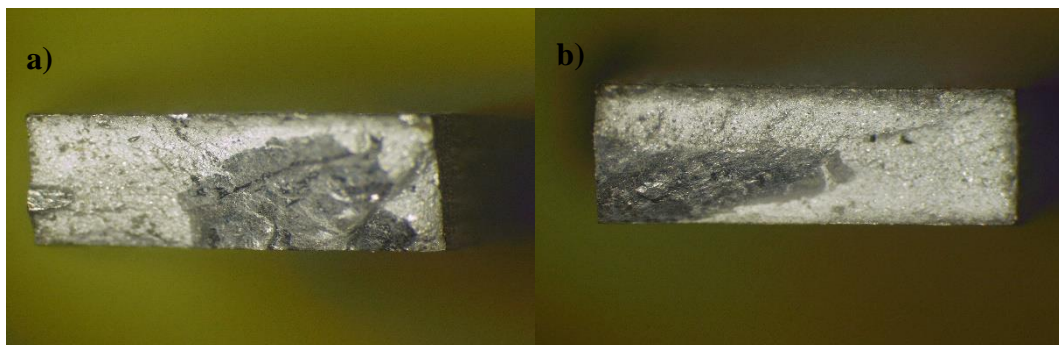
Superfícies de fratura dos provetes 4C (a) e 5A (b)
